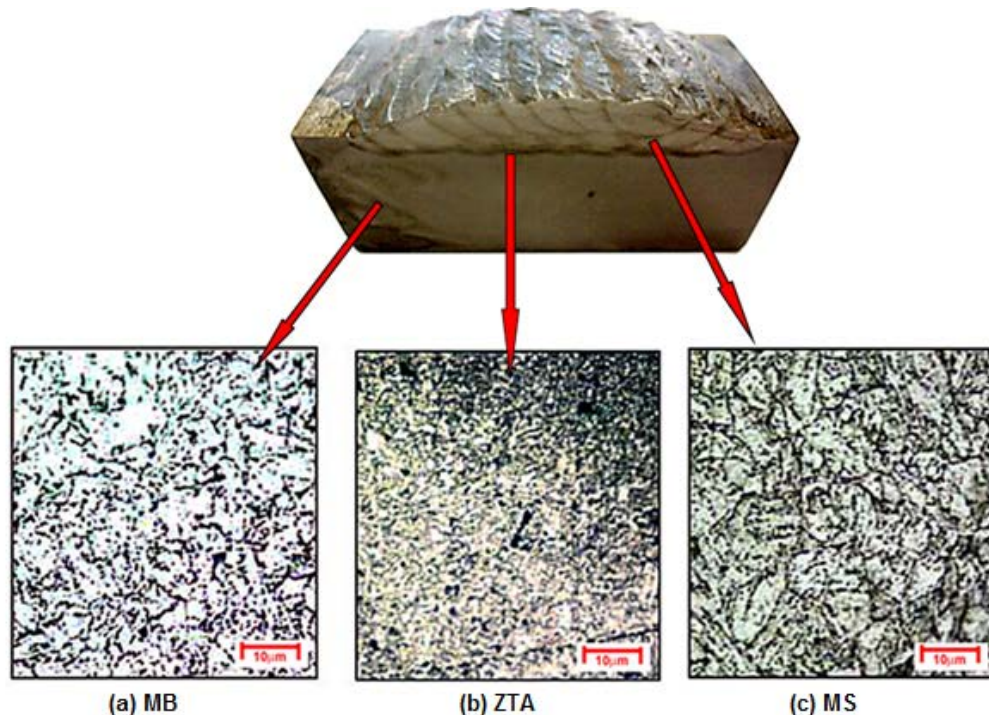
Soldagem eletrodo revestido – corpo de prova com passe de revenimento: (a) metal base (1000x) (b) ZTA (1000x) e (c) metal de solda (1000x).
